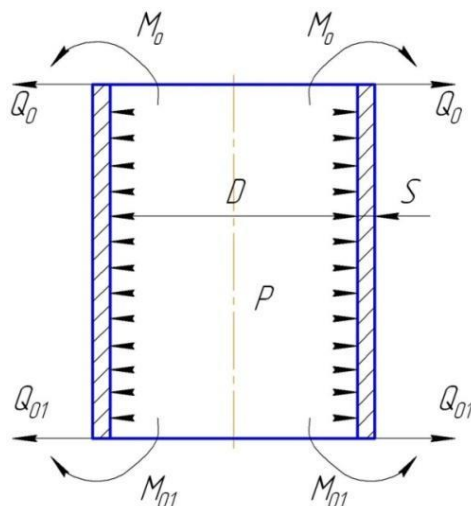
Схема розрахунку на міцність одношарової циліндричної обичайки
